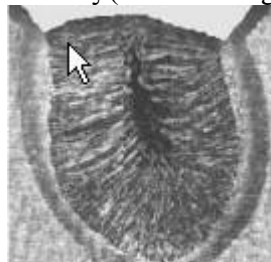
Cold Cracking defect SMAW (Technical Sheet 42, EWF)
